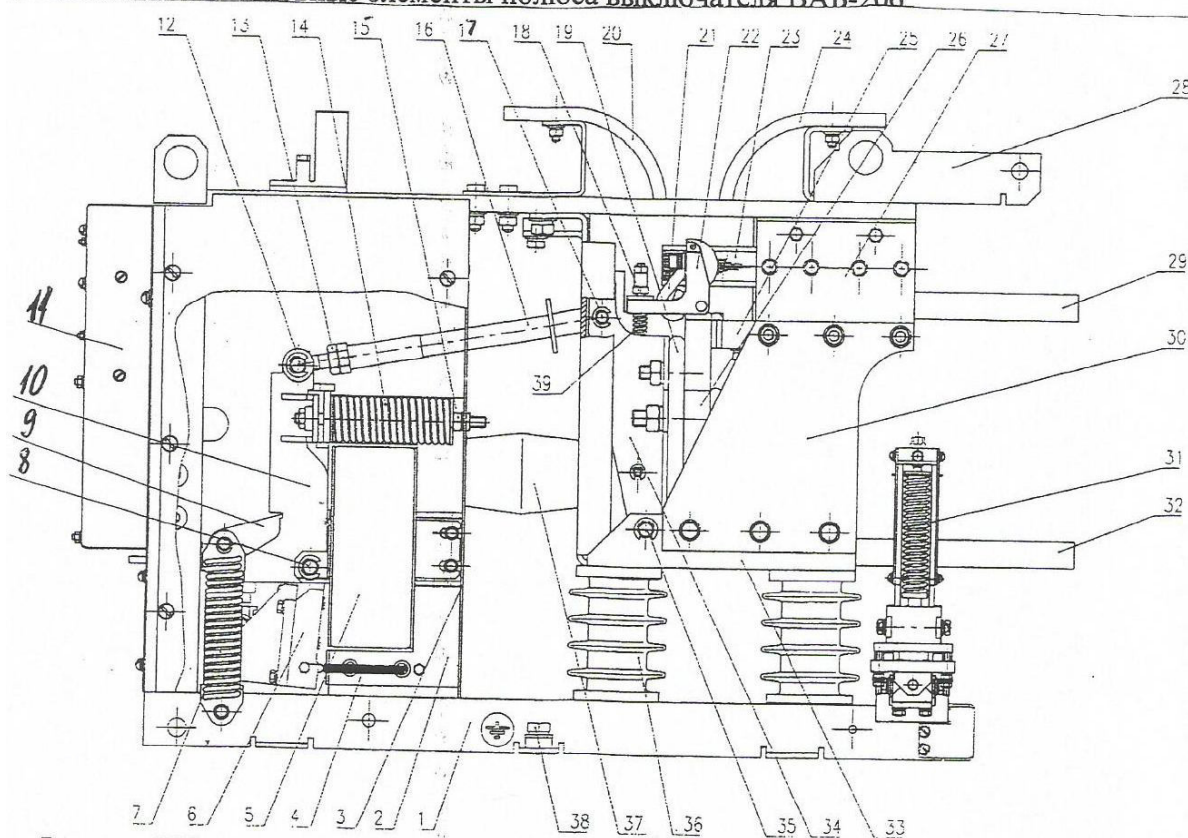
Конструкция полюса выключателя ВАБ-206
